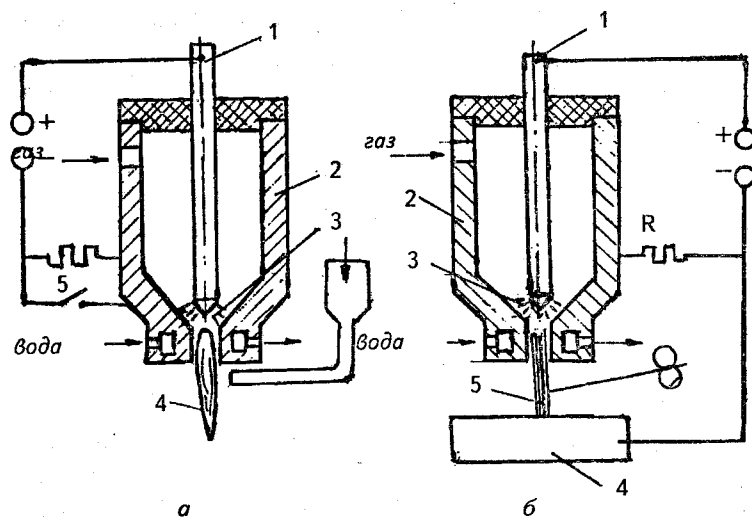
Схема плазменной наплавки дугой косвенного а и прямого б действия
